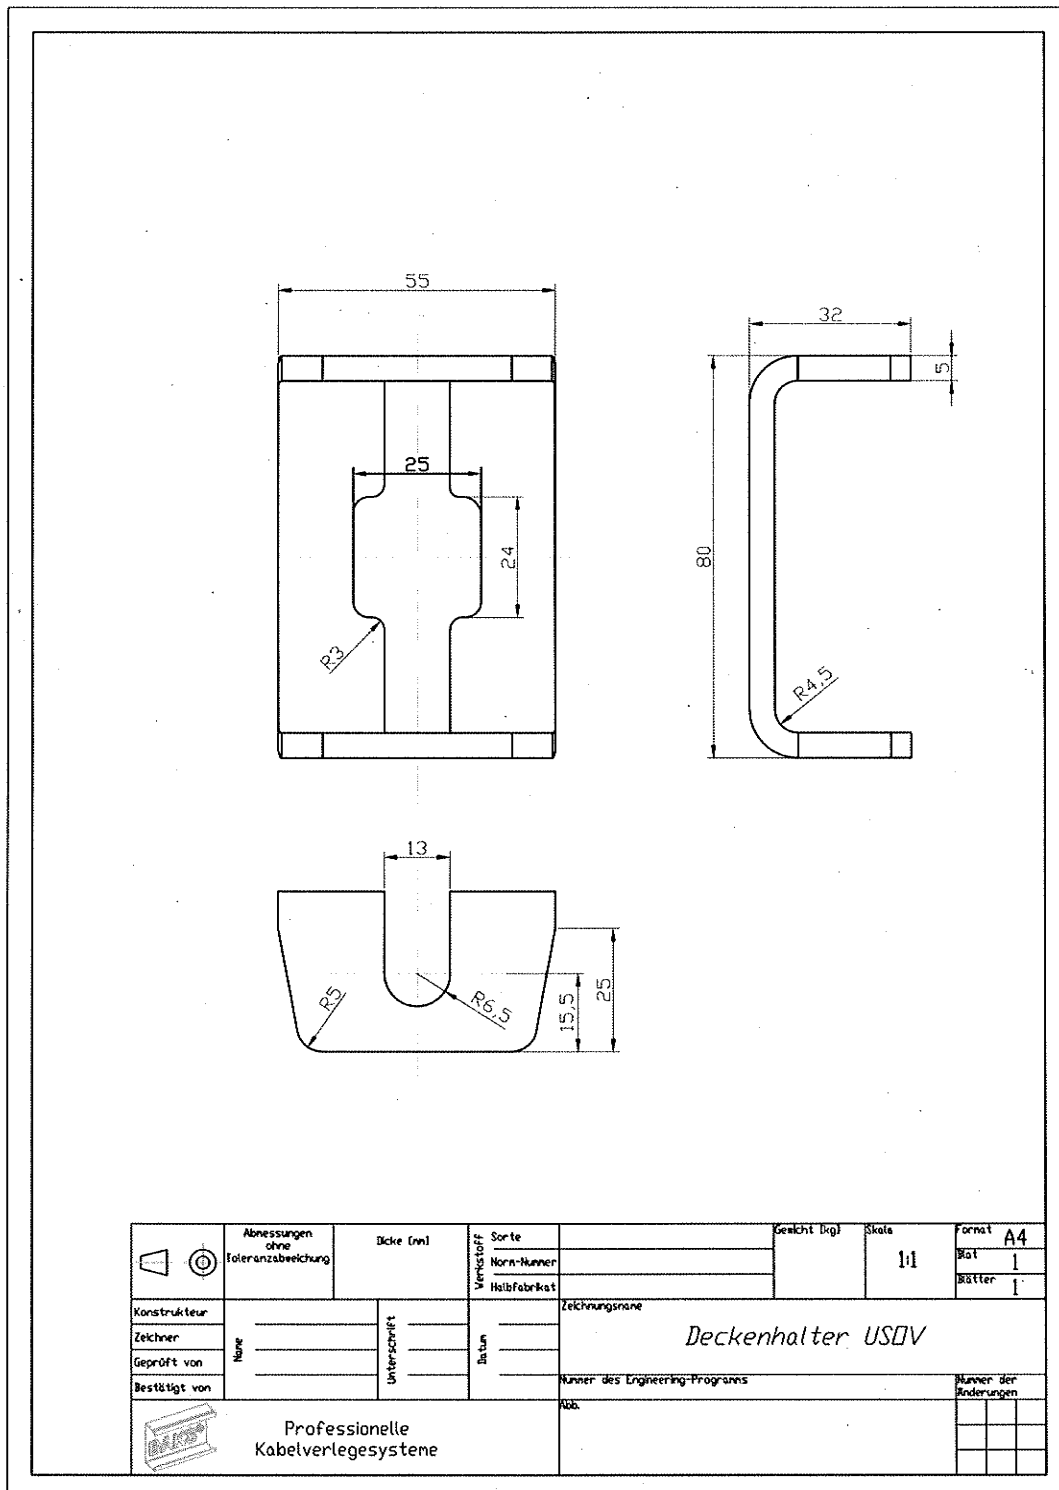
5 Deckenbefestigung der Gewindestange USOV
